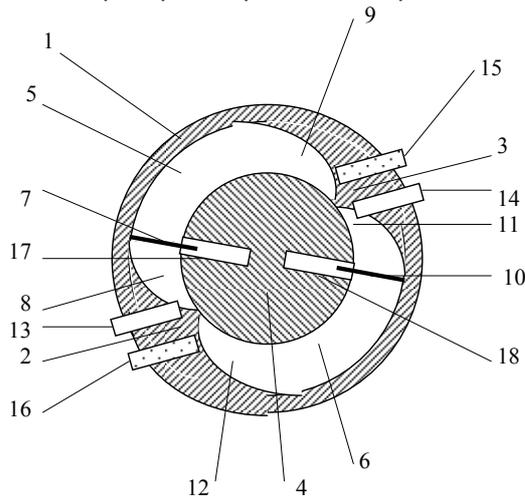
Схема нового парового двуполостного роторно-поршневого тор-двигателя
